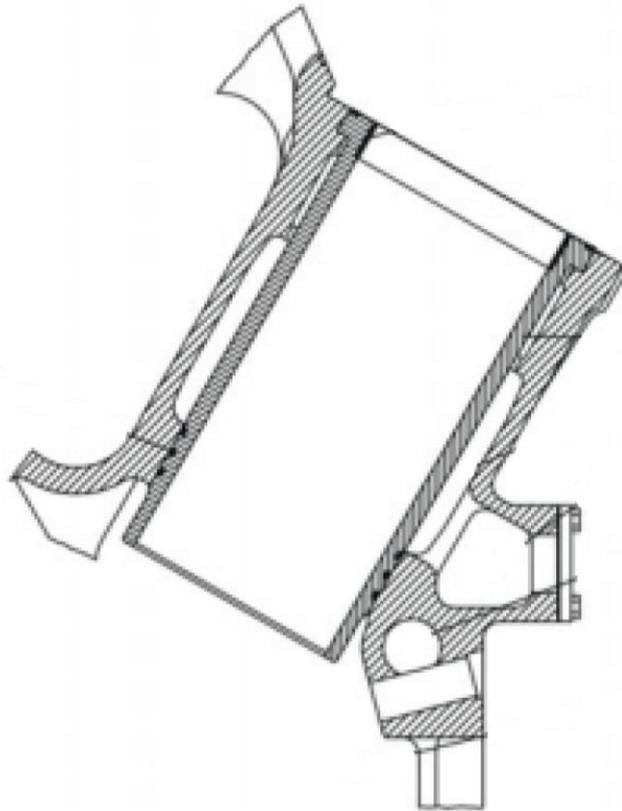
Втулка цилиндра подшипников закалены и тонко отшлифованы. Коренной подшипник принимает на себя осевую нагрузку коленчатого вала. Смазка коренного подшипника происходит через масляные каналы в картере. На одном конце коленчатого вала установлен сбалансированный маховик с зубчатым колесом стартера, на другом конце – виброглушитель (рисунок 2).
